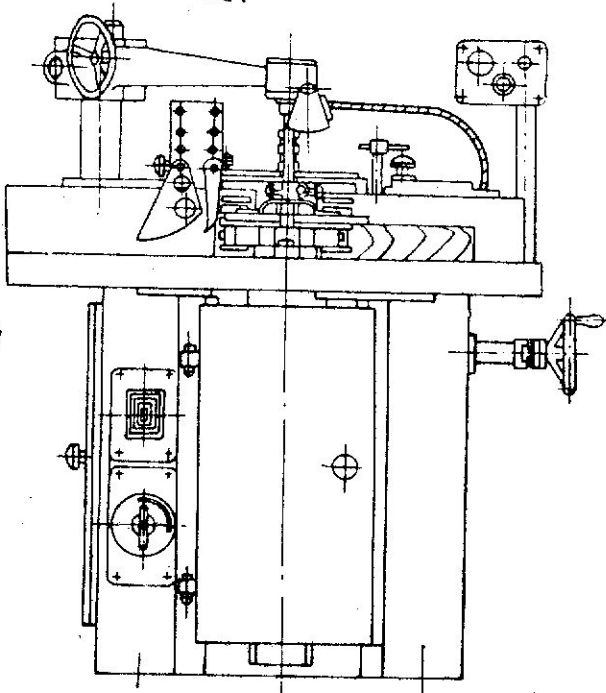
Станок фрезерный одношпиндельный модели ФС-1.
